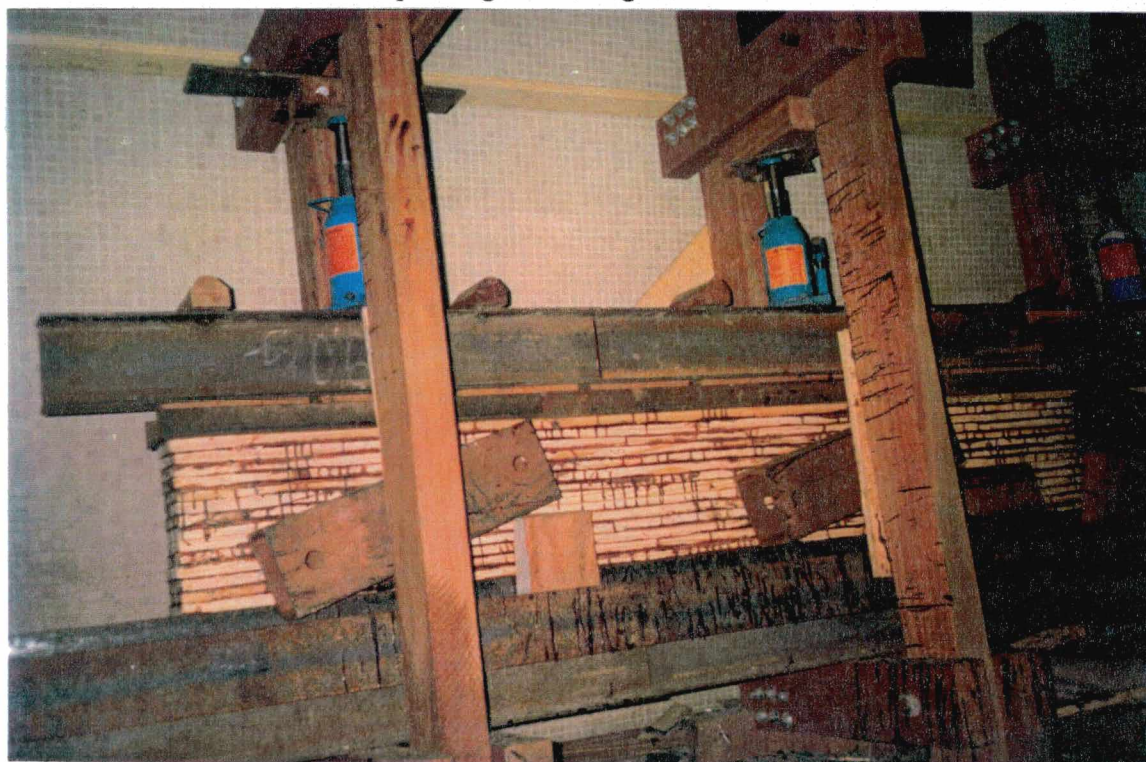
Ilustração do dispositivo de prensagem das vigas.
